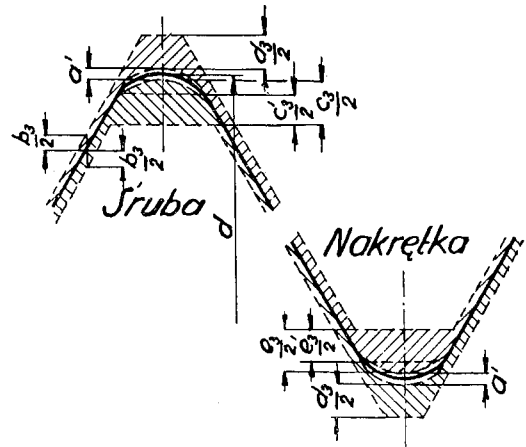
Tolerancje niemieckie (DJN) dla gwintu metrycznego, pasowania średniego i zgrubnego.
